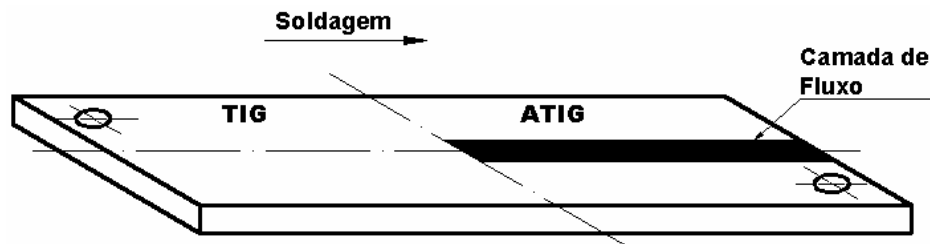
Corpo de prova mostrando a direção de soldagem e a camada de fluxo simples aderida à superfície do corpo de prova.
